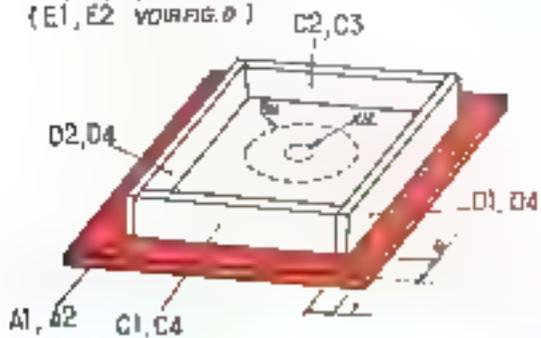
Explorent de montage de la carte PCB. Les pièces sont à assembler en double exemplaire de chaque côté de la carte à trois plans.
